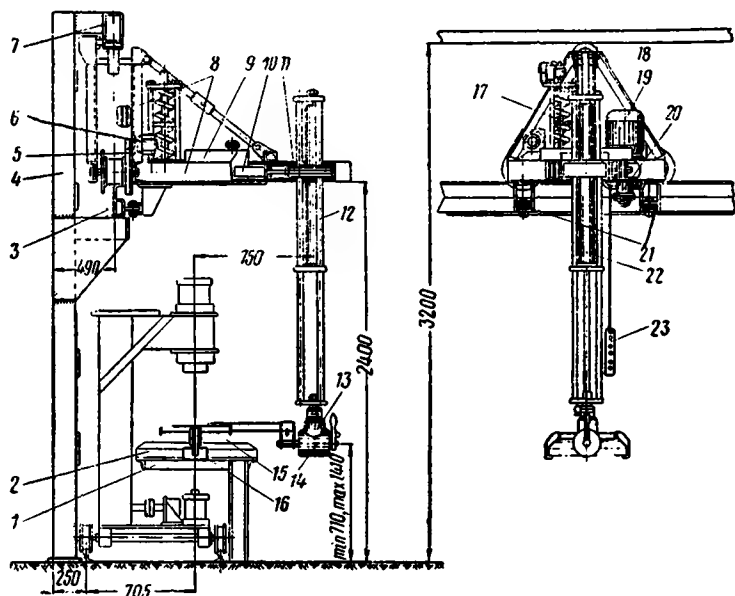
Приспособление «механическая рука» для монтажа полюсов в остоу тягового двигателя и стенд для запрессовки сердечников полюсов в катушки:
